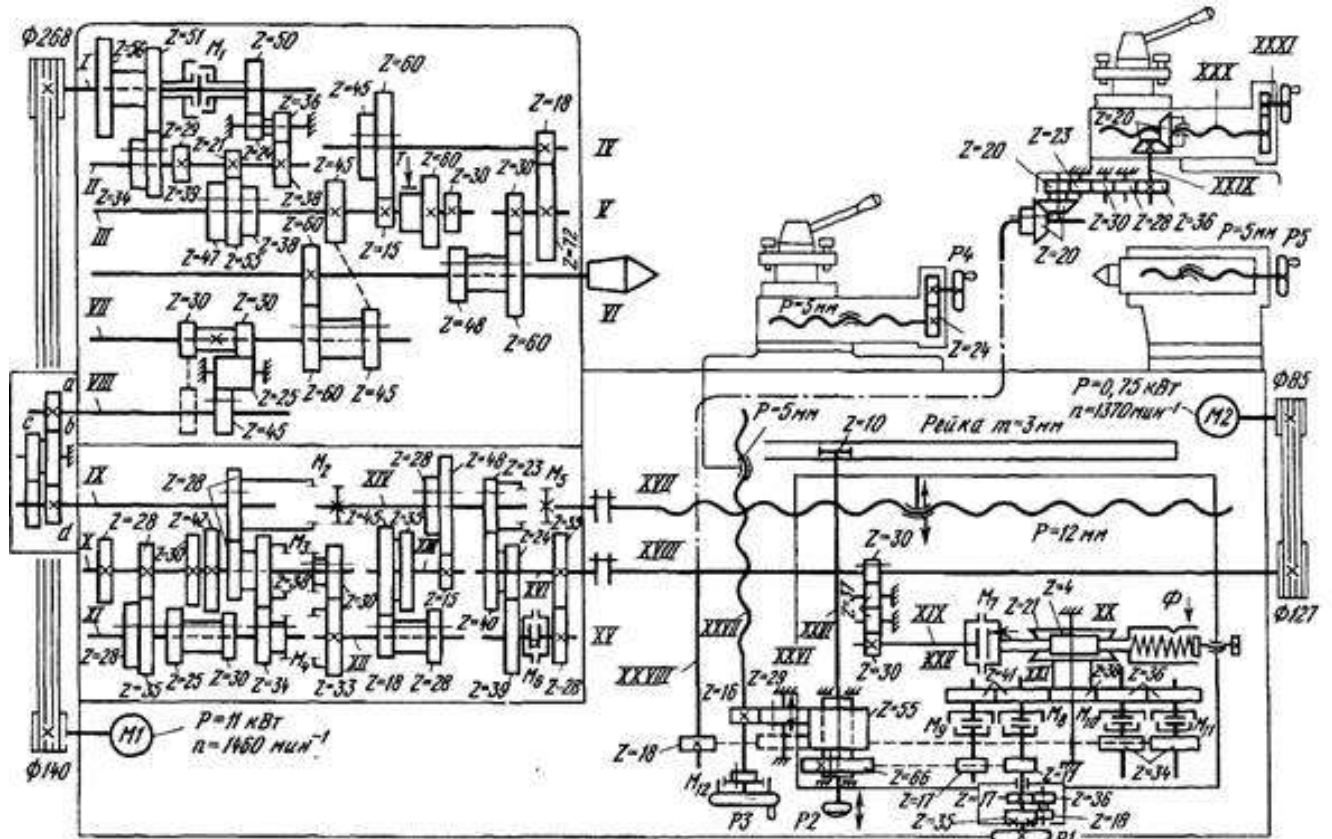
Кінематична схема токарно-гвинторізного верстата 16К20
